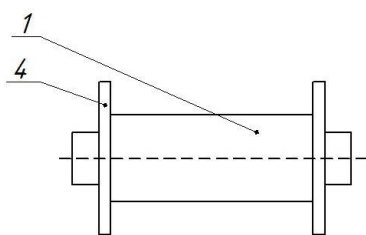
Ливарно-прокатной валок с буртиками [10]:
